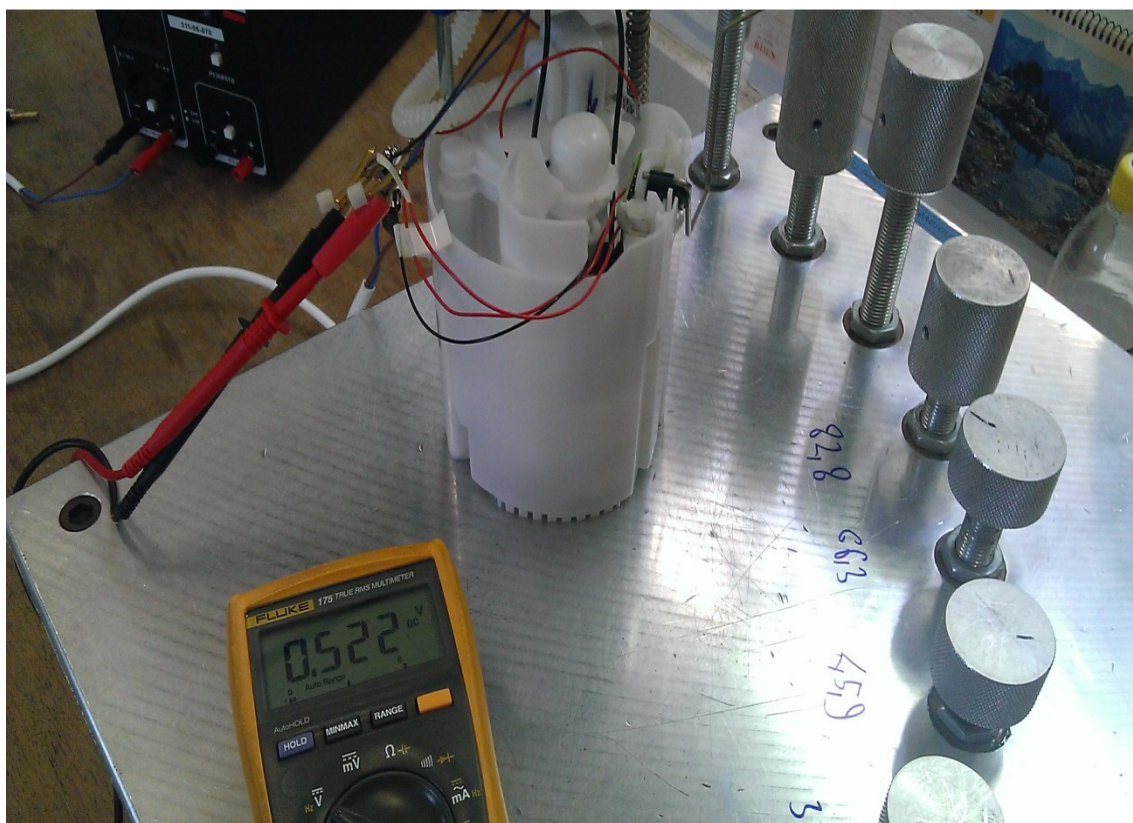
Měřící sestava- stabilizovaný zdroj, měřící přístroj, dorazová stolice a čerpadlový modul, foto autor.
